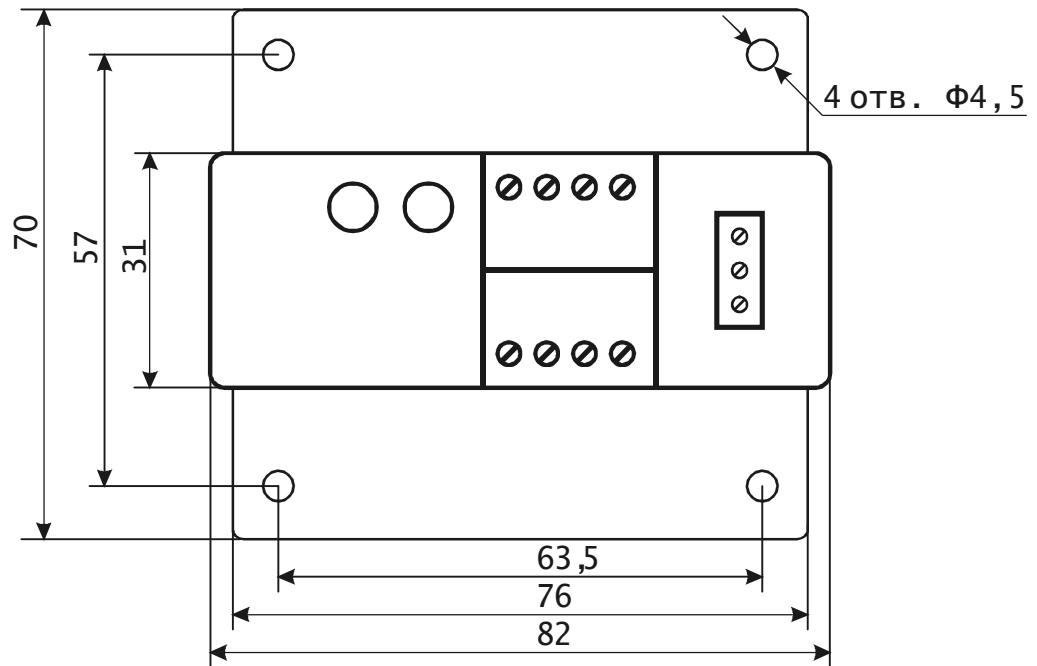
Габаритный чертеж ИП-40020-1-0
